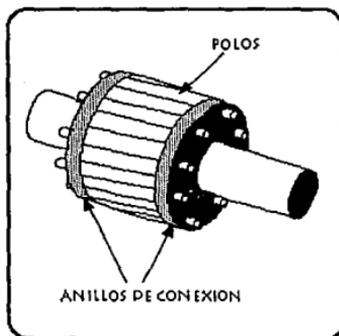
ROTOR COMPLETO TIPO JAULA DE ARDILLA DE BARRAS INCLINADAS.
